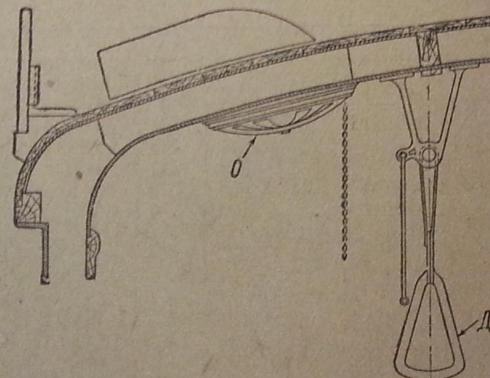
Вентиляция вагона со сводчатой крышей: *O* — вентиляционное окно, *D* — держатель ременный.
